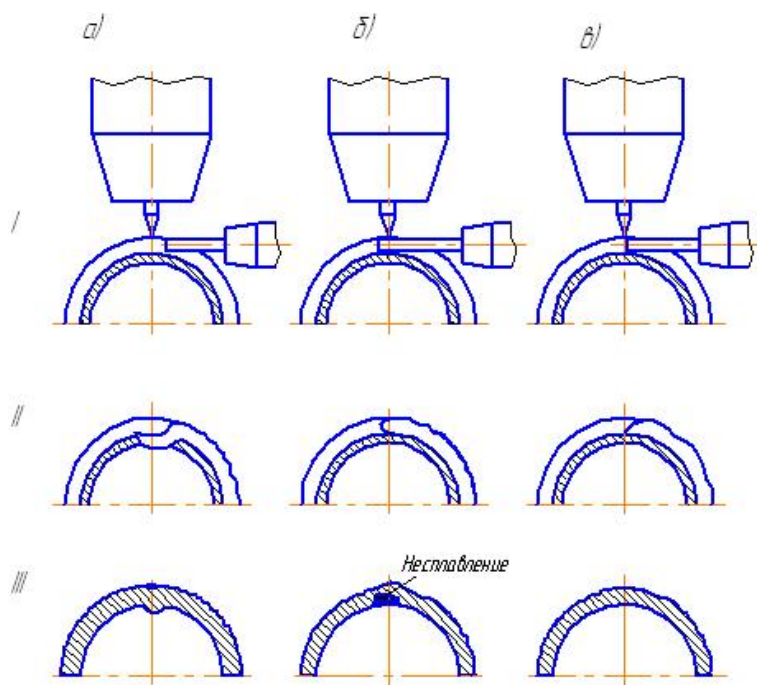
Положение присадки по отношению к электроду в момент начала сварки: а, б) неправильное положение; в) правильное положение; I – подготовительный период; II – начало сварки; III – окончание сварки
